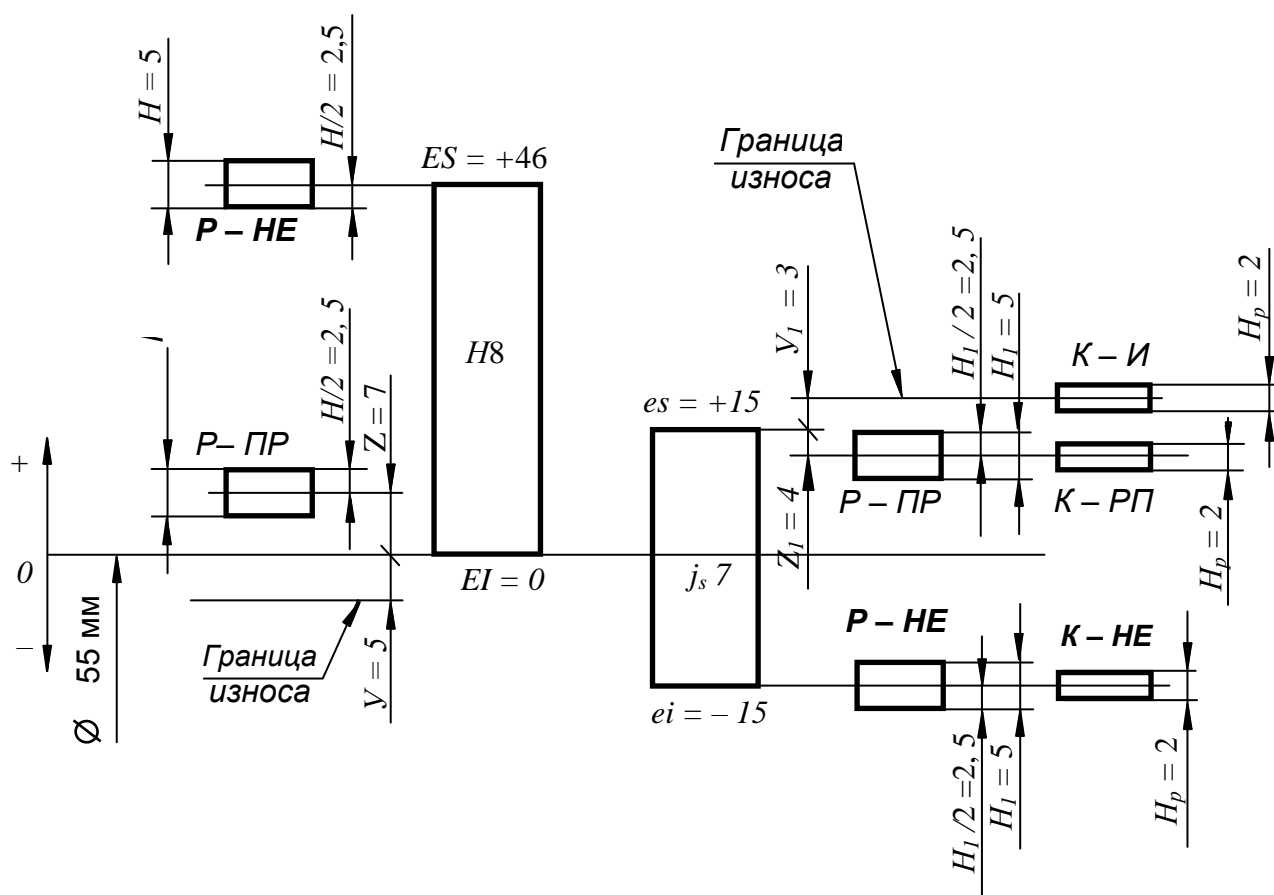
Схемы полей допусков калибров для контроля деталей соединения $\varnothing 55 H8/js7$
